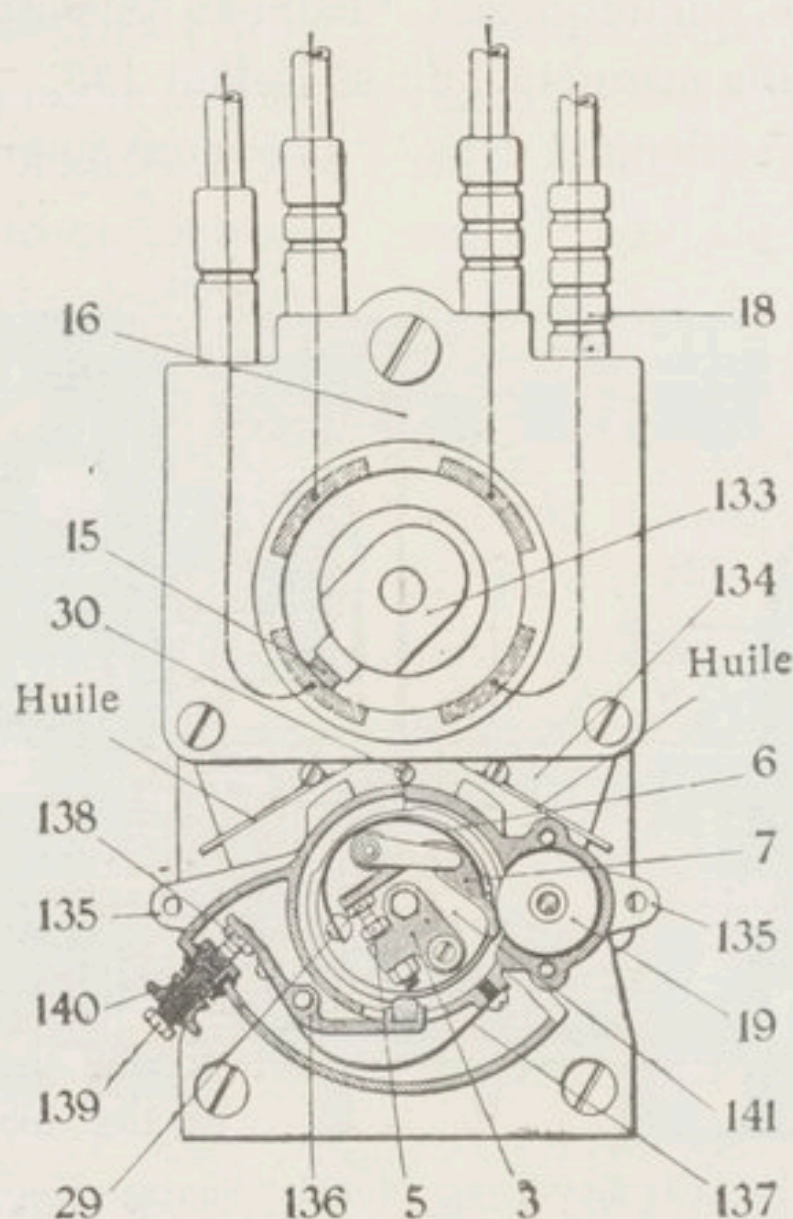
Vue arrière d'une magnéto Bosch pour double allumage.
